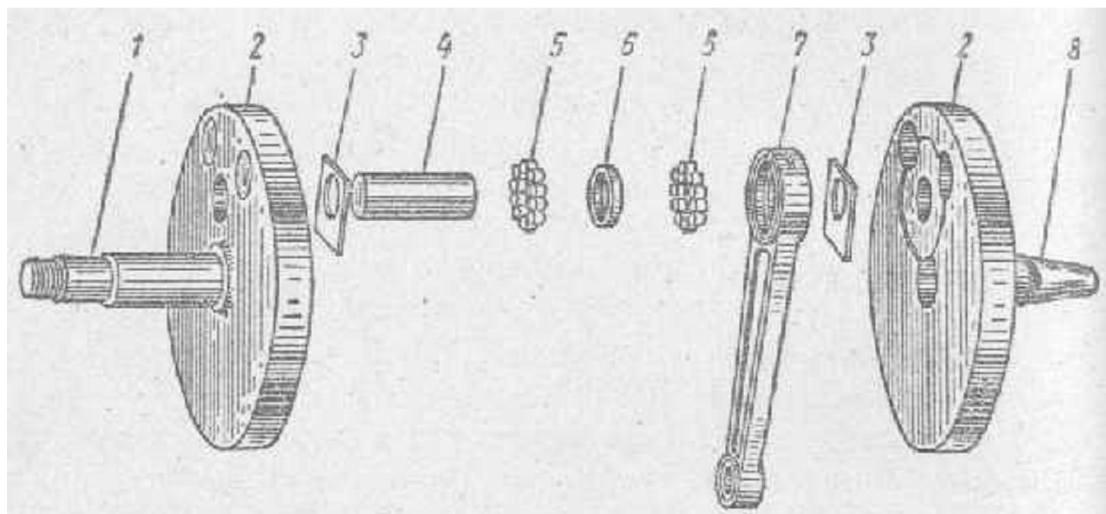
Детали коленчатого вала одноцилиндрового двигателя мотоцикла ЯВА-250:
